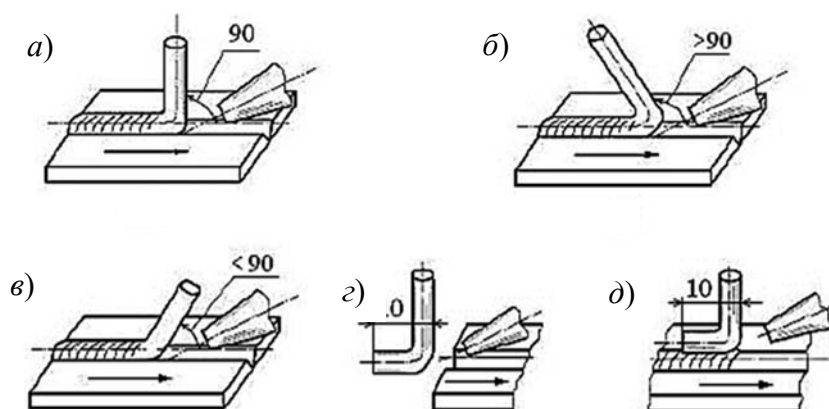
Положение присадочного прутка и горелки при сварке
